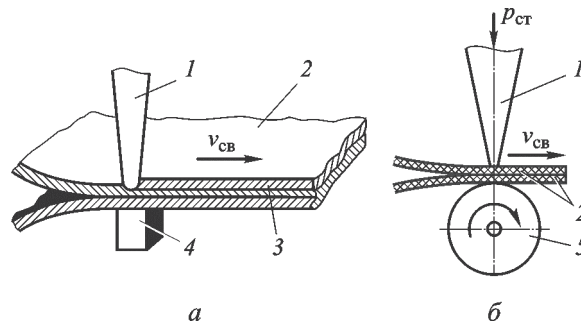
Схемы шовной УЗС «на протяг» (а) и на вращающемся ролике-опоре (б): 1 — волновод-инструмент; 2 — свариваемые пленки; 3 — сварной шов; 4 — неподвижная опора; 5 — ролик-опора;  $v_{св}$  — скорость сварки;  $p_{ст}$  — сварочное статическое давление
